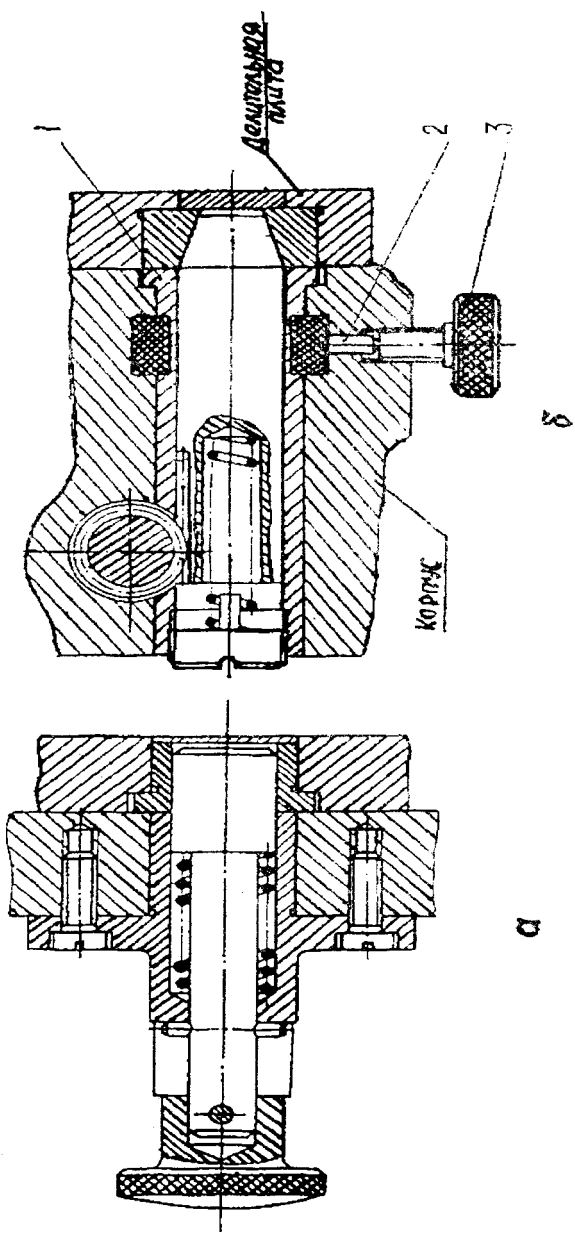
Конструкции фиксаторов: а - цилиндрического (обычного);
